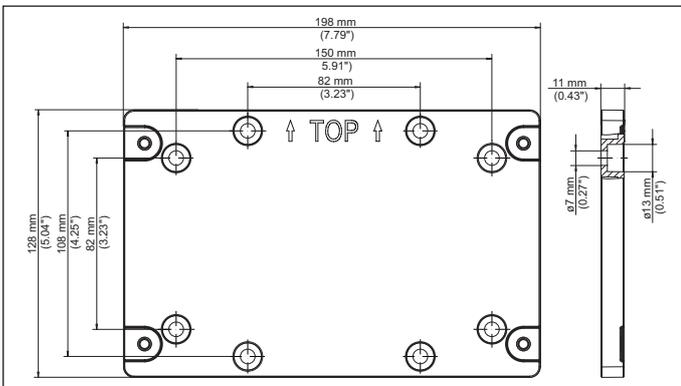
Dimensiones placa de montaje VEGAMET 861, 862
